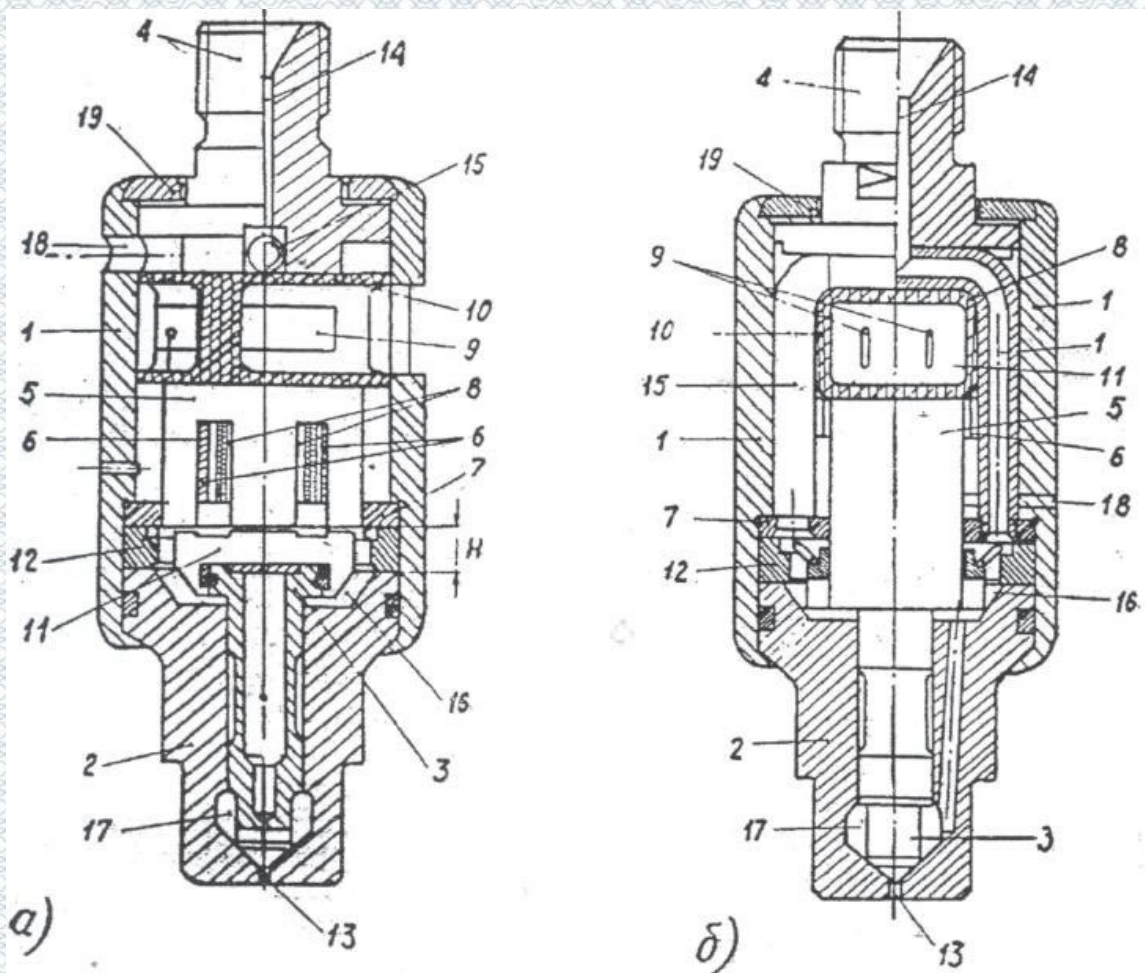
Конструкція електромагнітної форсунки фірми Roto Diesel
